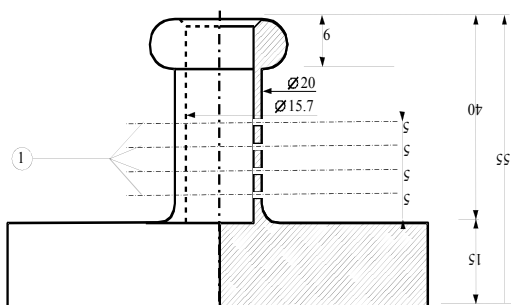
Cilindro oco de bronze, fechado de um lado; Plano e corte vertical, dimensões em mm
